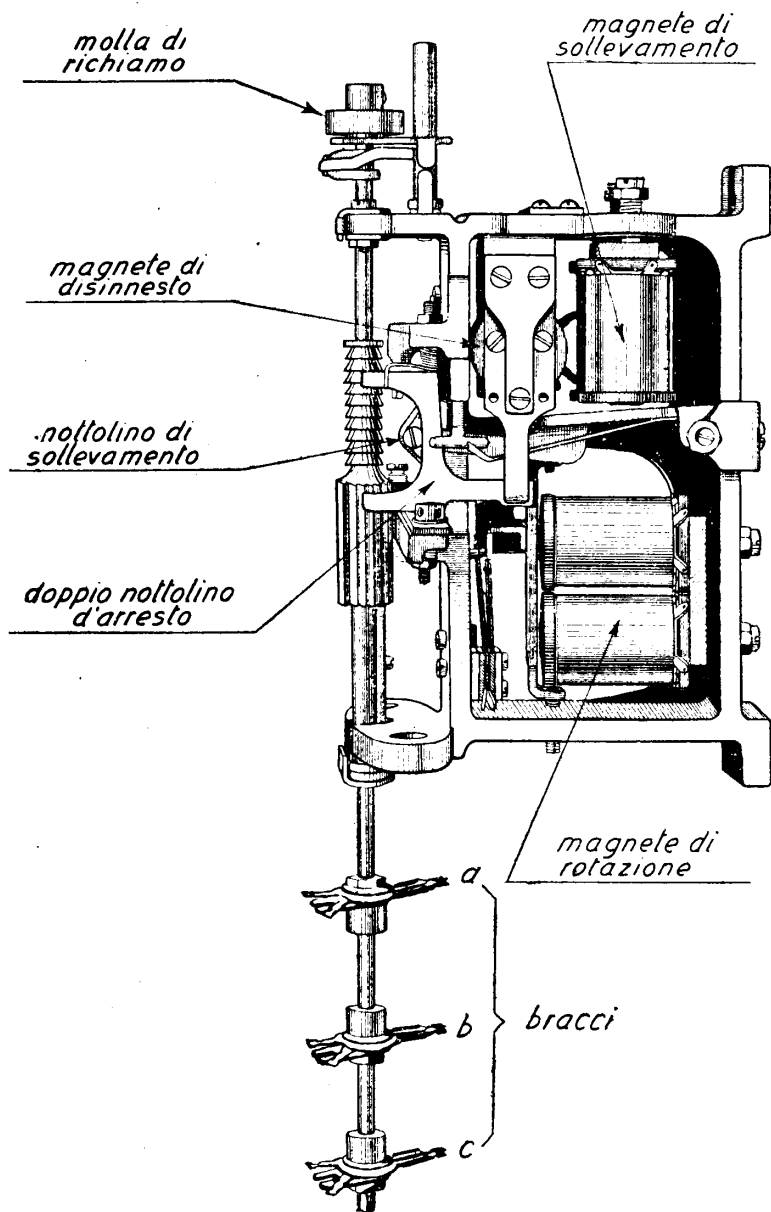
Equipaggio mobile e meccanismo del selettore Siemens-Strowger.
